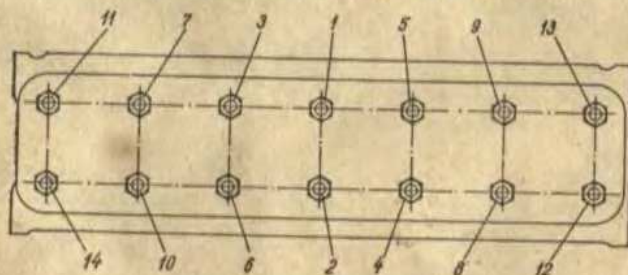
Порядок затяжки гаек головки цилиндров двигателей ЯАЗ-М206
